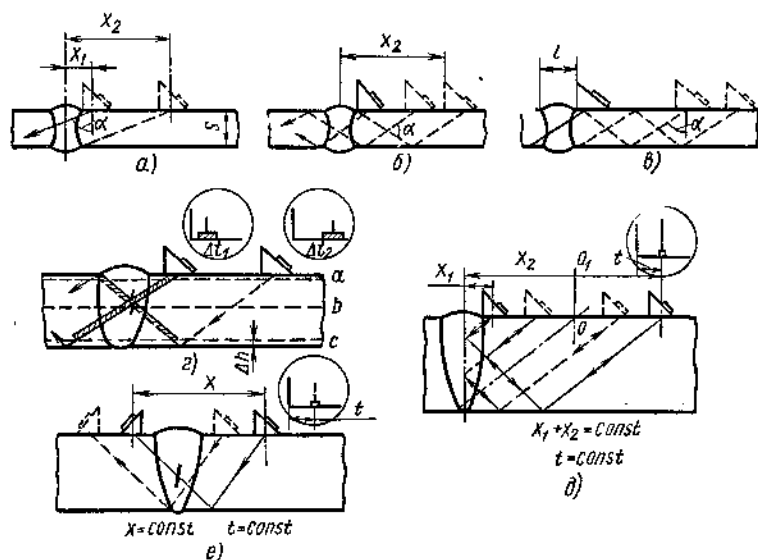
Схемы прозвучивания стыковых сварных швов:
